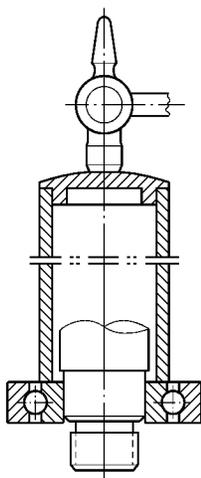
38 用锤直接击打滚动轴承的拆卸方法
